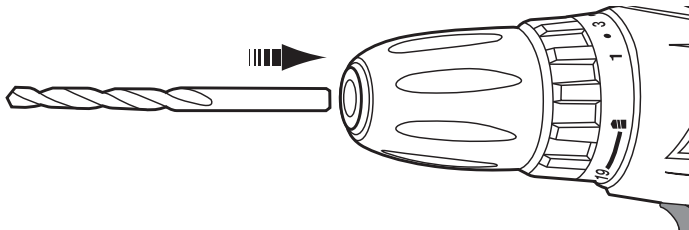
, Bohrer können direkt in die Werkzeugaufnahme eingeführt werden.
